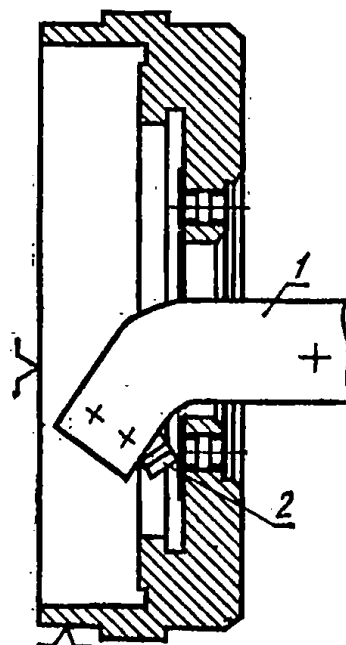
Схема обработки выступающих сварочных швов со стороны закрытого торца:
